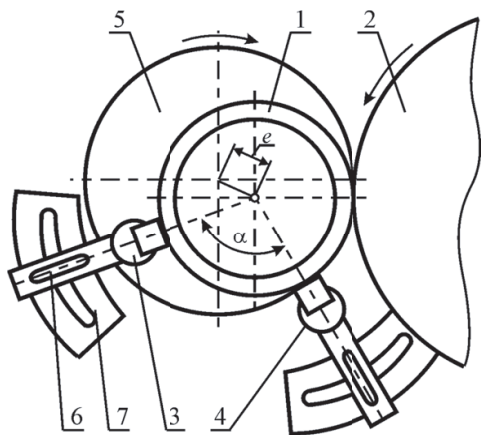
Схема шлифования дорожки качения кольца подшипника:
